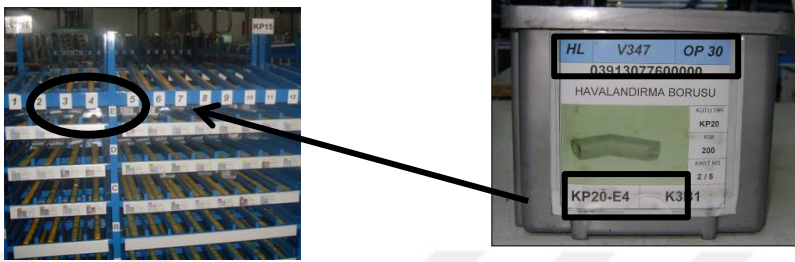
Giriş Ambarına yapılan ‘malzeme toplama alanı
